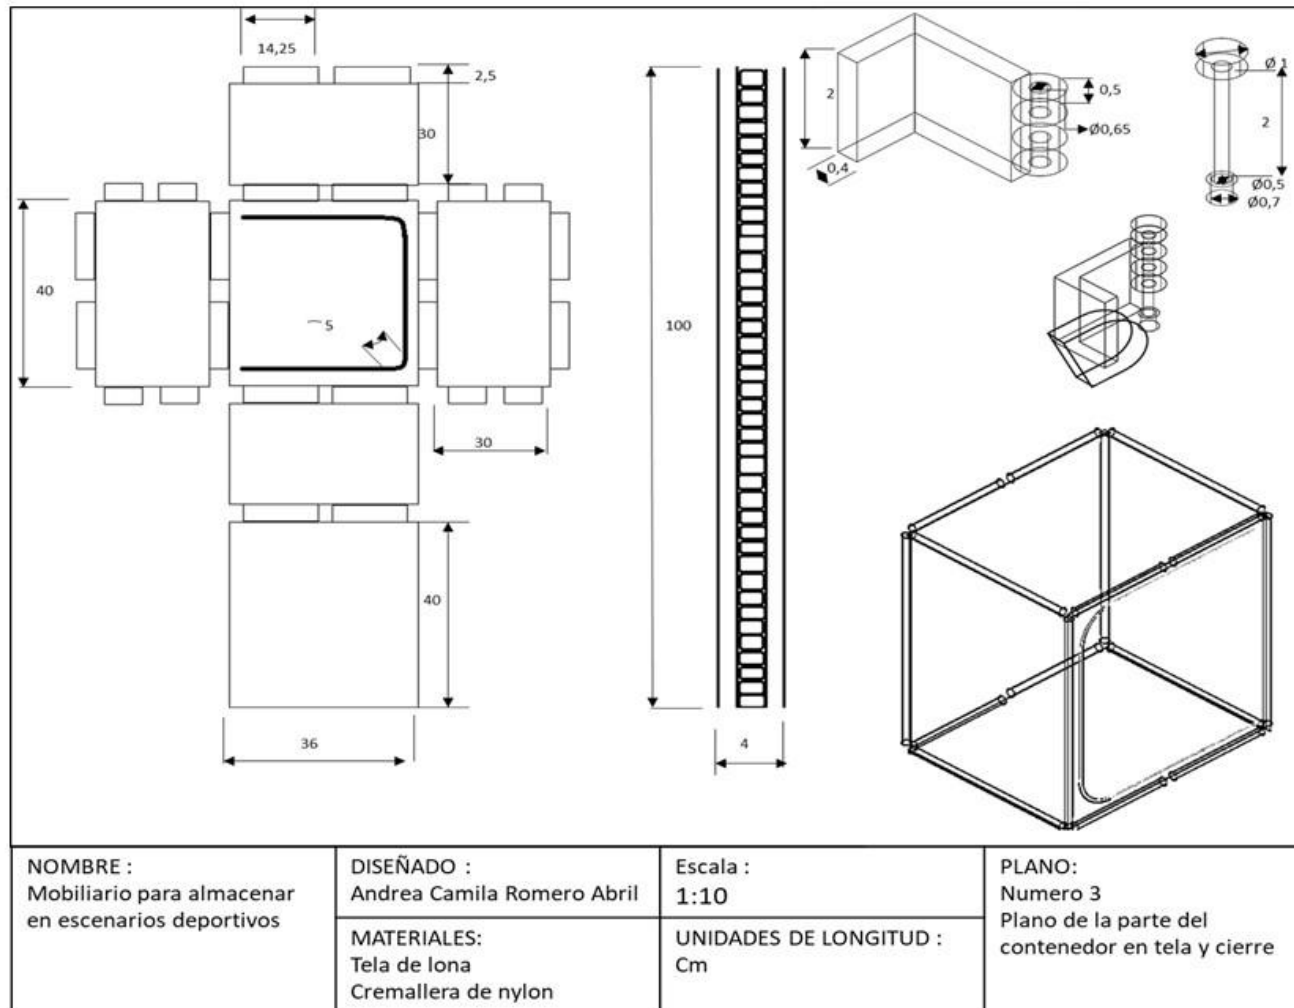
Plano de la parte del contenedor . Fuente: Elaboración propia
